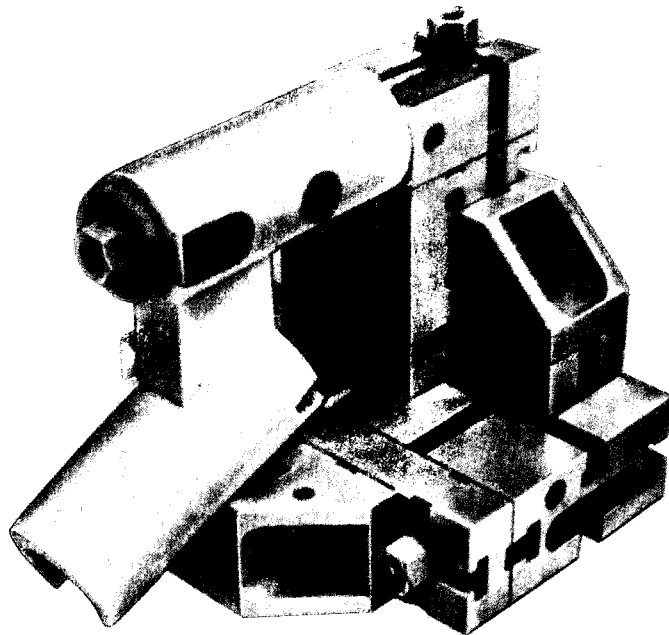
Приспособление для фрезерования набором фрез бобышек головки
